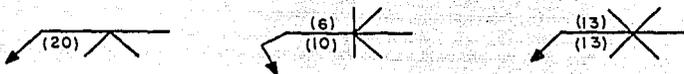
→ DESIGNACION DE GARGANTA EFECTIVA DE SOLDADURAS COMBINADAS
